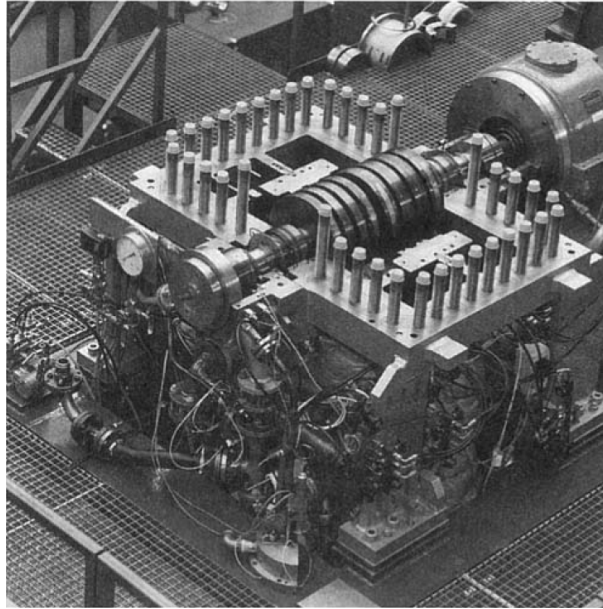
Compresseur avec rotor d'essais [17].
